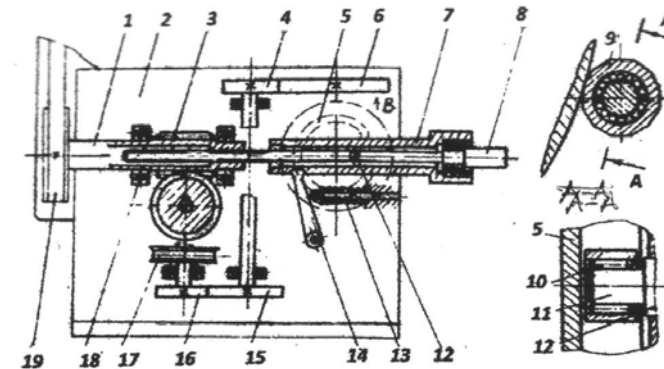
Передаточний механізм привода плоскокулачкової силової головки для подрібнення зливної стружки
